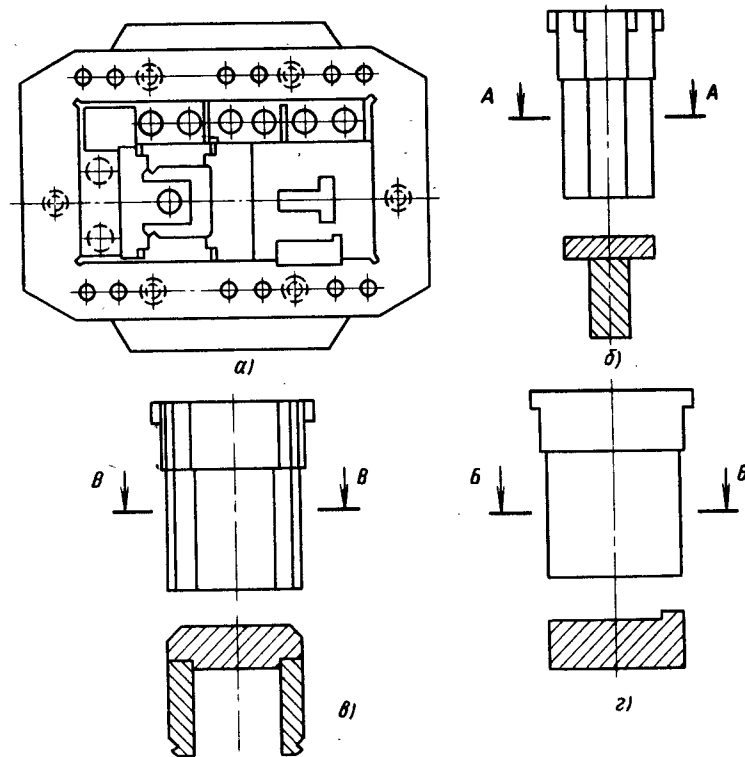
Твердосплавный штамп типа ТШ-336
